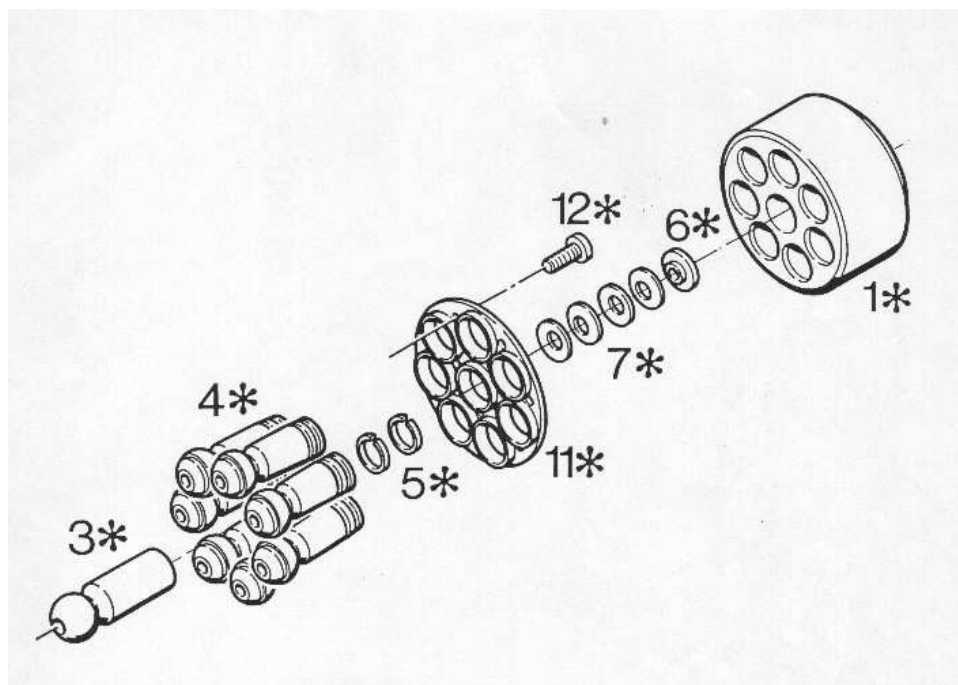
Vue éclatée de l'ensemble rotor Hydrostatique11, élément hydraulique
